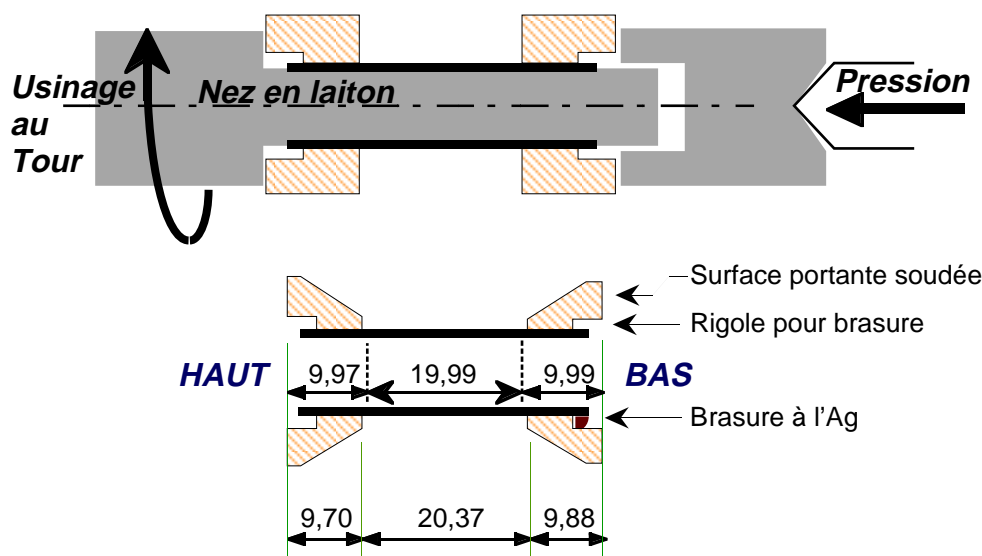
Paroi latérale. Principe de l'usinage, emplacement des soudures et brasures, et cotes définitives (cotes à l'ambiante, compter typiquement 0,3 % de contraction à froid)
